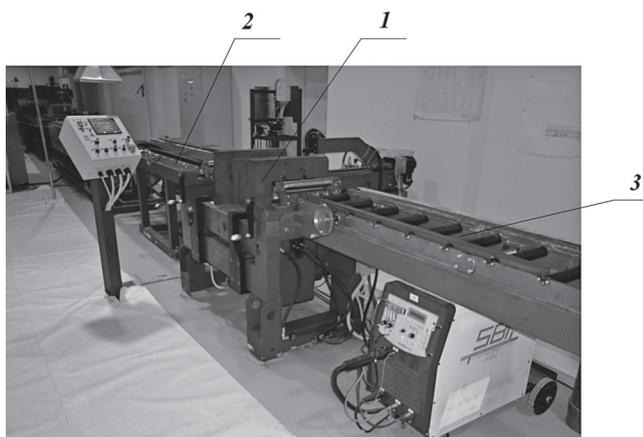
Схема расположения агрегата формирования рулонов: 1 – установка стыкосварочная; 2 – стол с линейками левый; 3 – стол с линейками правый
